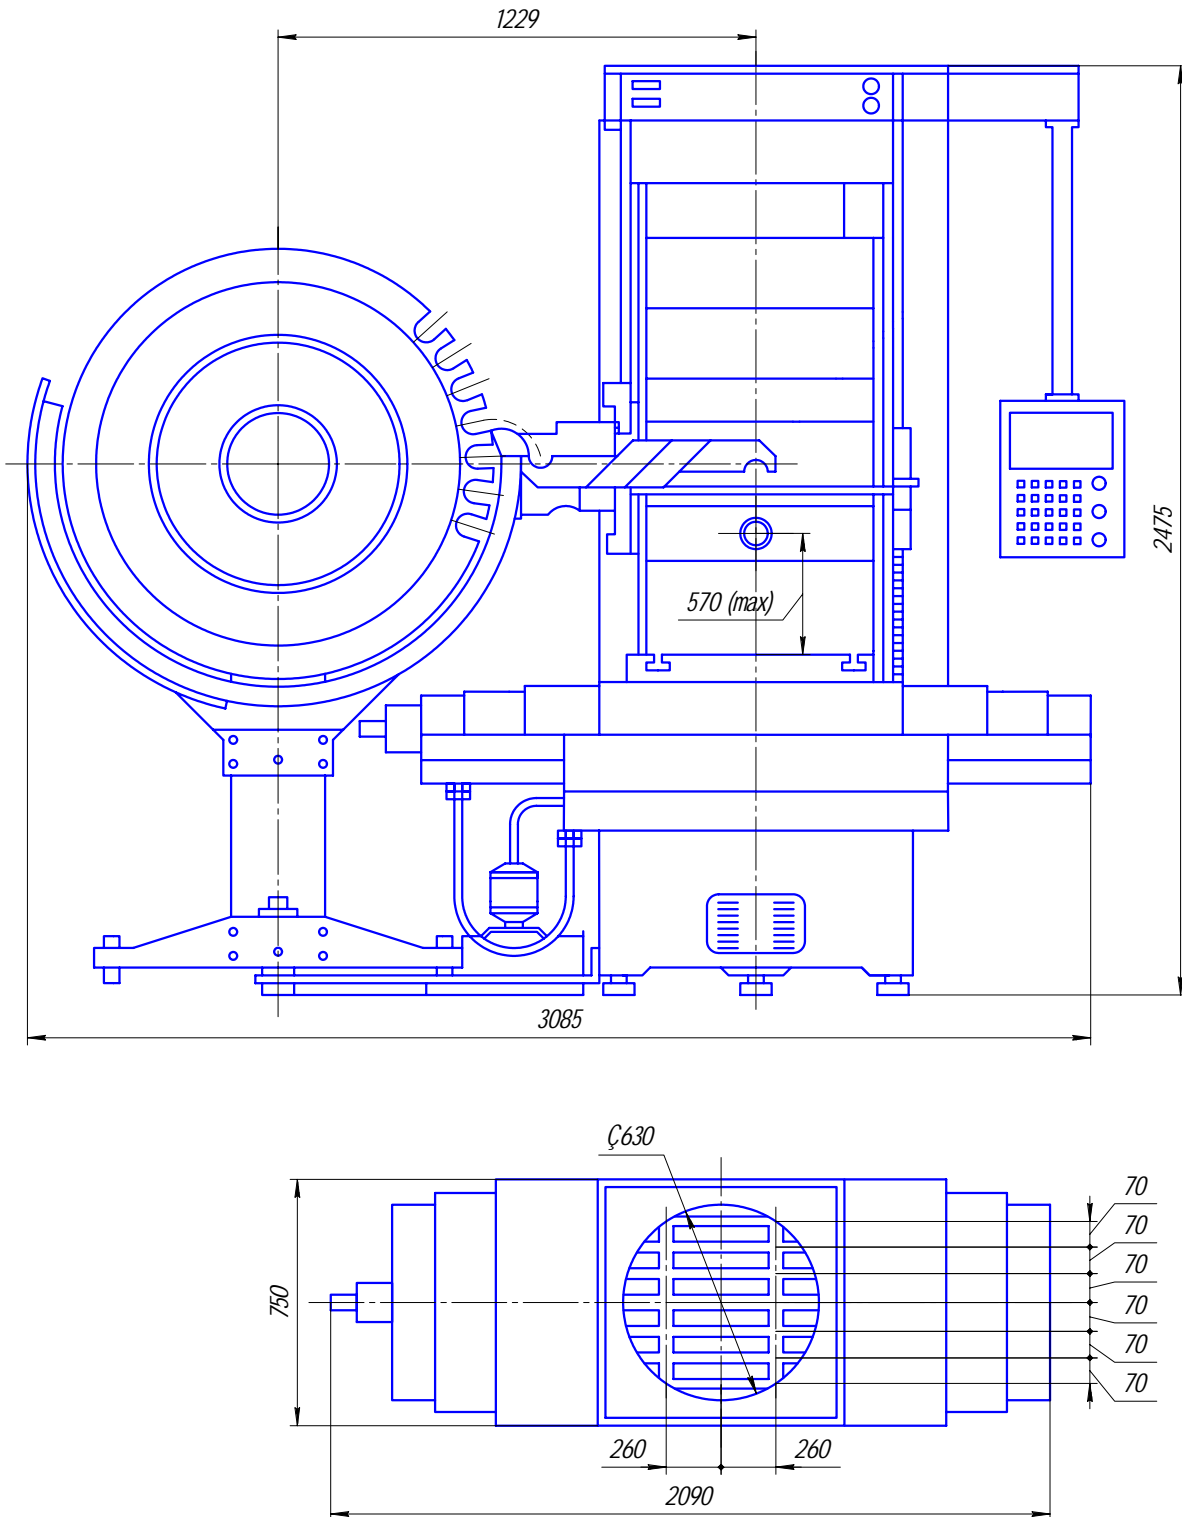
Габарити робочої зони і установочні бази свердлильно-фрезерно-розточного верстата з ЧПК моделі 2204ВМФ4
